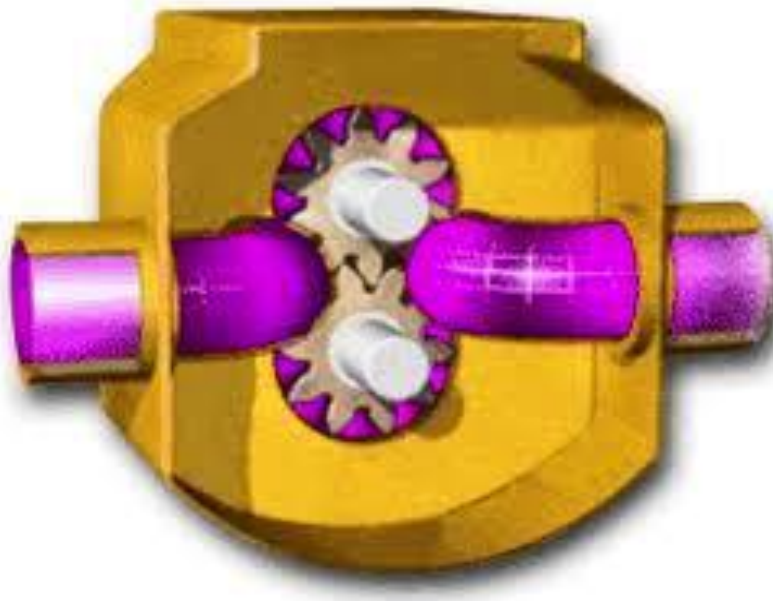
BOMBA DE ENGRANAJES EXTERNOS.
